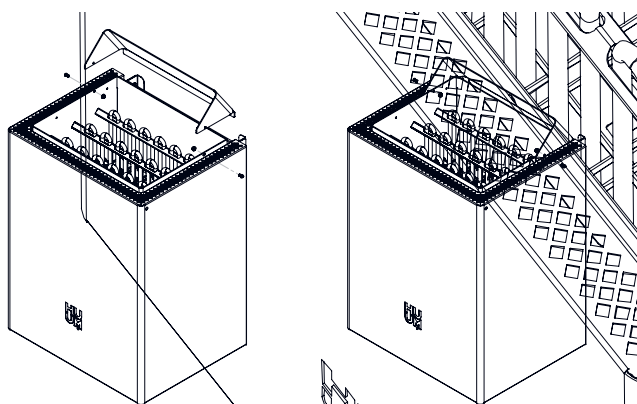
Installation du dispositif de retenue du HUUM CORE Wall et CORE Wall Combi.
